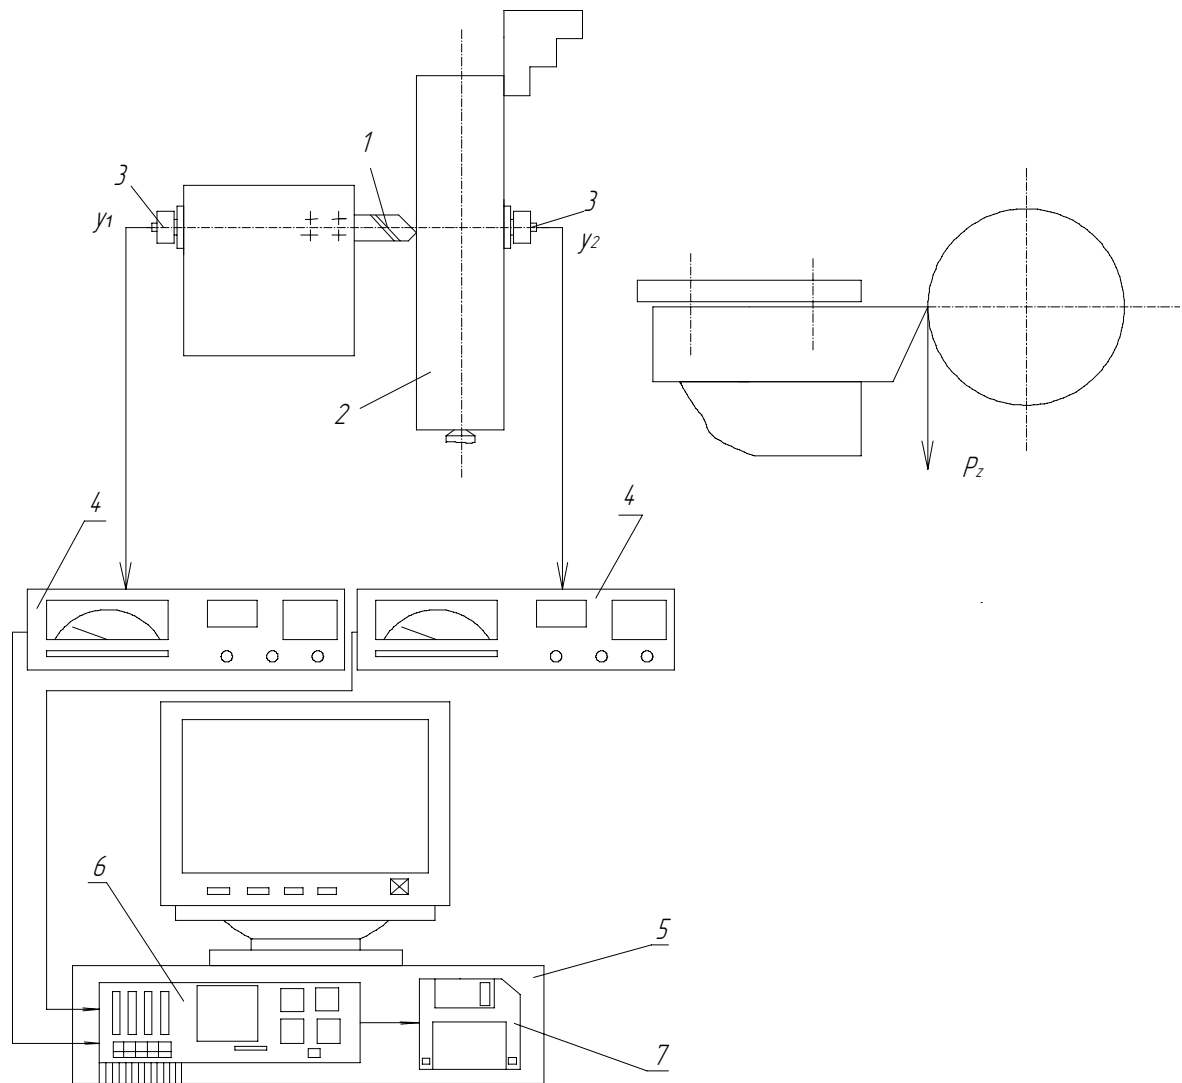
Схема вимірювання коливань у робочій зоні токарного верстата:
